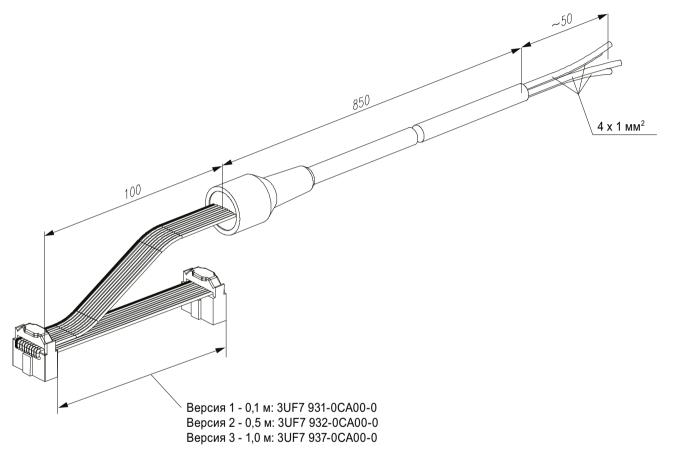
Габаритный чертеж Ү-образного соединительного кабеля
